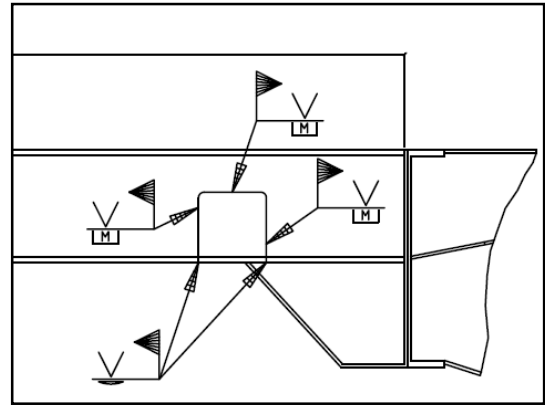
Schweißnahtübersicht für Pos.1
